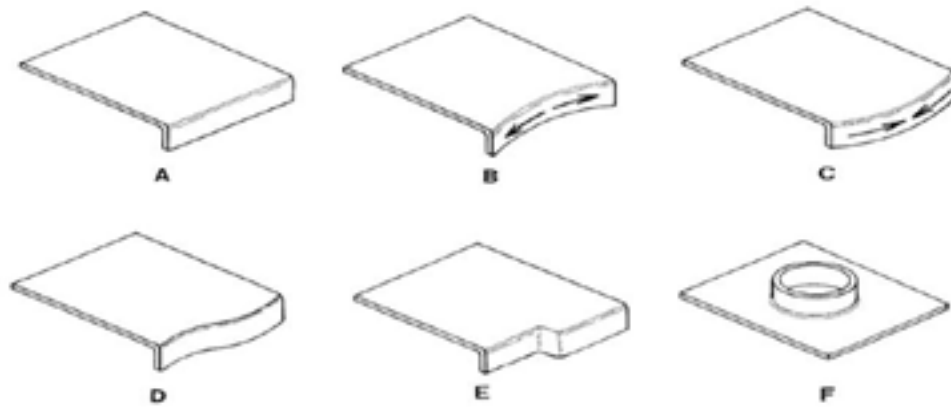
Operações que caracterizam a conformabilidade de bordas. As formas básicas de flangeamento (A, B e C) e flangeamento combinado (D, E e F) [8].
